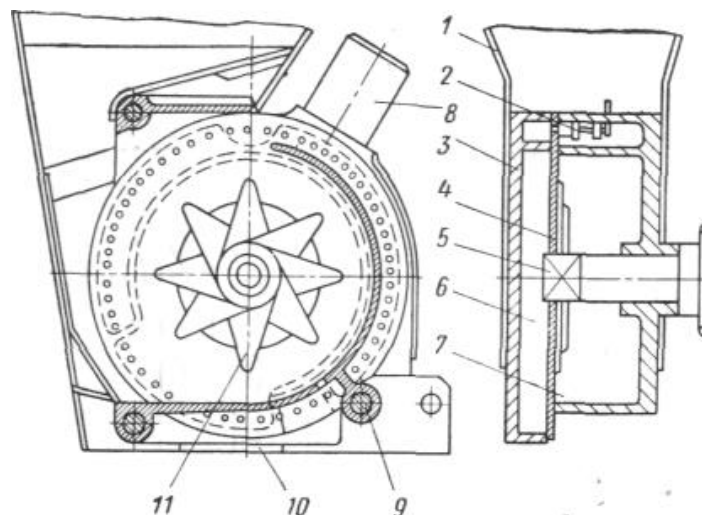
Висівний апарат сівалки «СПЧ-6»: 1- бункер; 2- очищувач насіння; 3- корпус вакуумної камери; 4- висівний диск; 5- вал приводу; 6- камера розрідження; 7- насіннева камера; 8- патрубок; 9- кріплення; 10- вікно скидання; 11- гумові диски.
